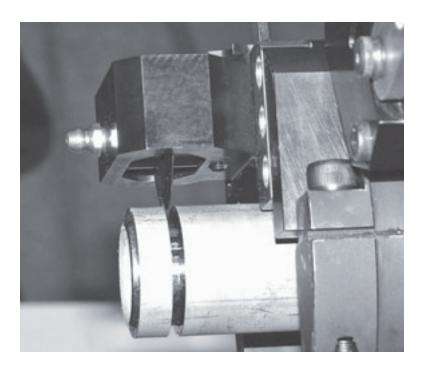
La molette doit se trouver juste au-dessus du diamètre extérieur de la coupe avant de démarrer la machine.
